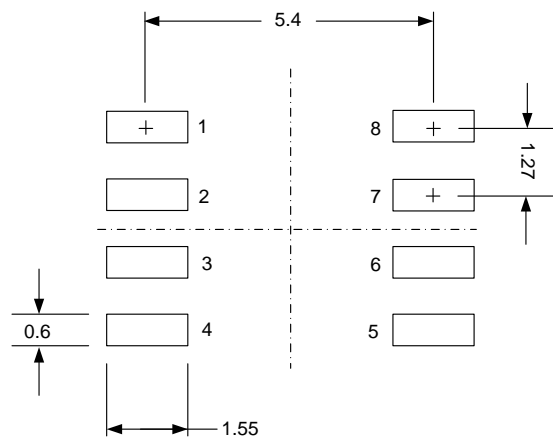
PCB 焊盘: SOP-8L (150 mil)
